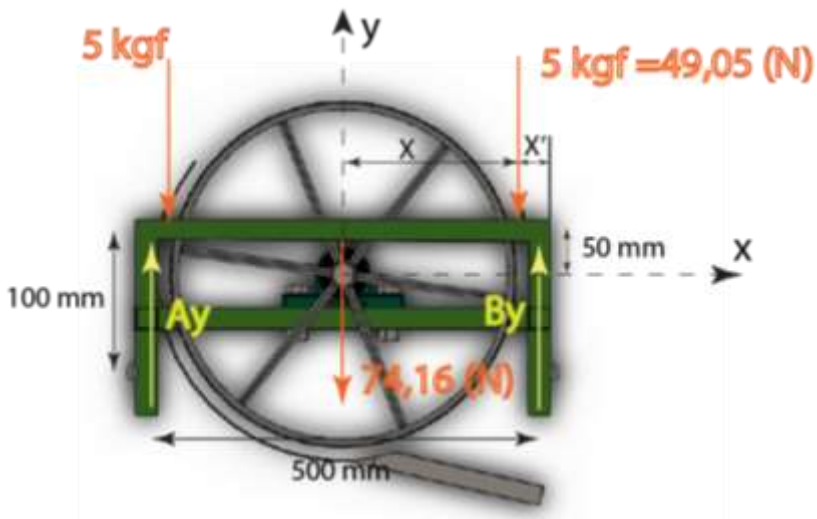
Fuerzas que actúan sobre la estructura plano x-y.
